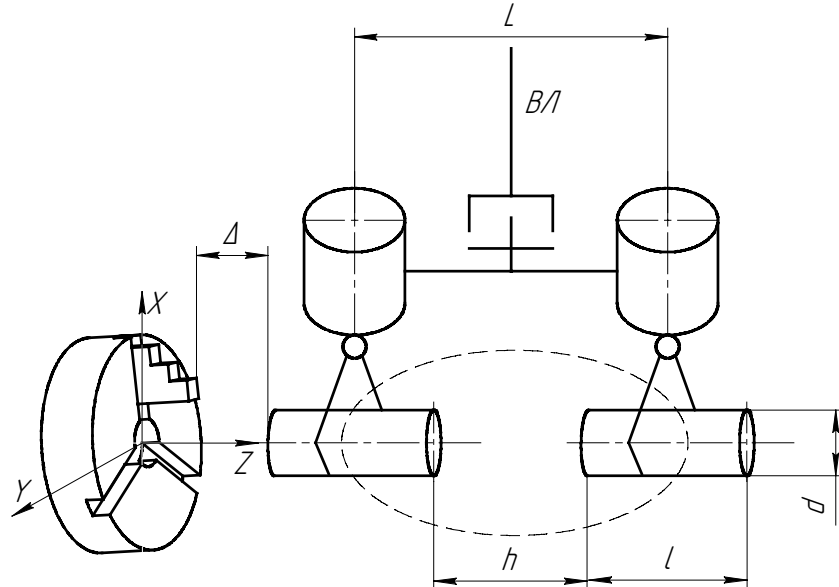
Розрахункова схема для визначення величини необхідного простору в робочій зоні верстату
